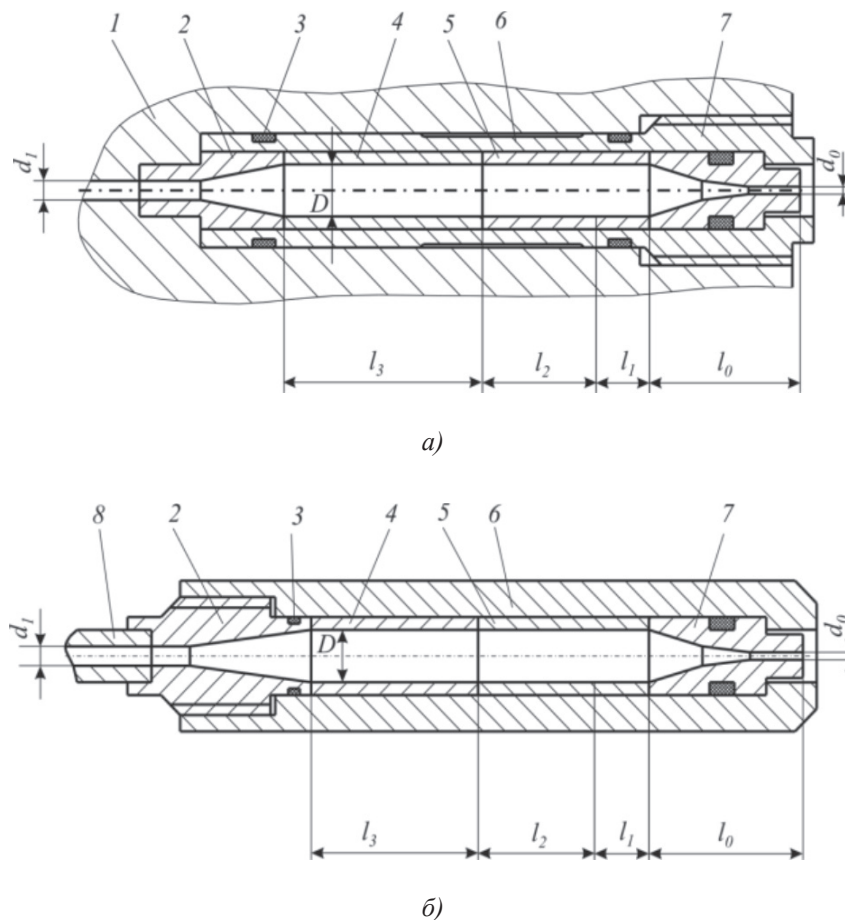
Конструкции малогабаритных струеформирующих устройств: а – с внутренним подводом воды; б – с наружным подводом воды: 1 – корпус исполнительного органа; 2 – диффузор; 3 – уплотнение; 4 – задняя втулка; 5 – успокоитель; 6 – корпус; 7 – насадка; 8 – водовод
